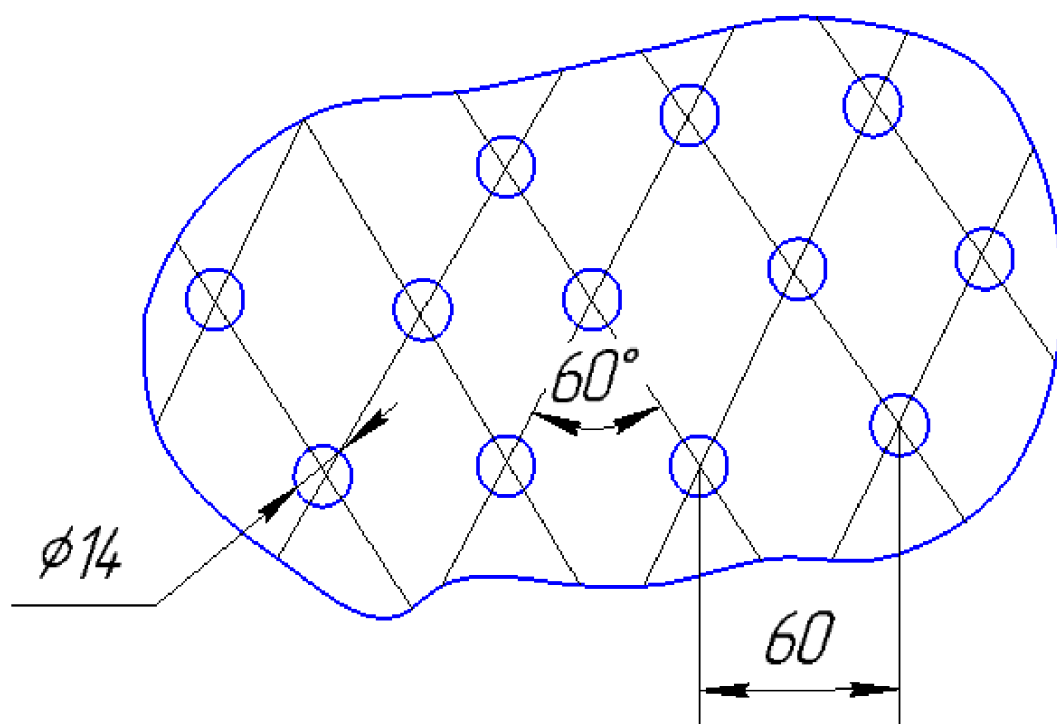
Предложенный чертеж сетчатой тарелки
